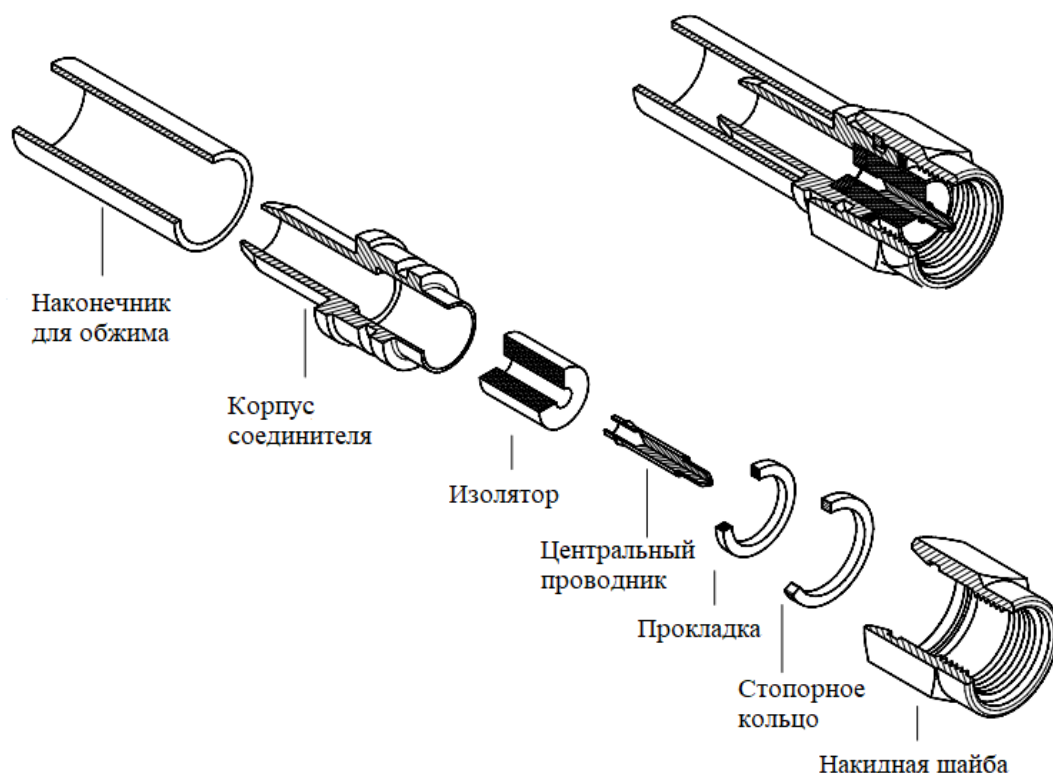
Внутреннее устройство коаксиального соединителя SMA [25]
